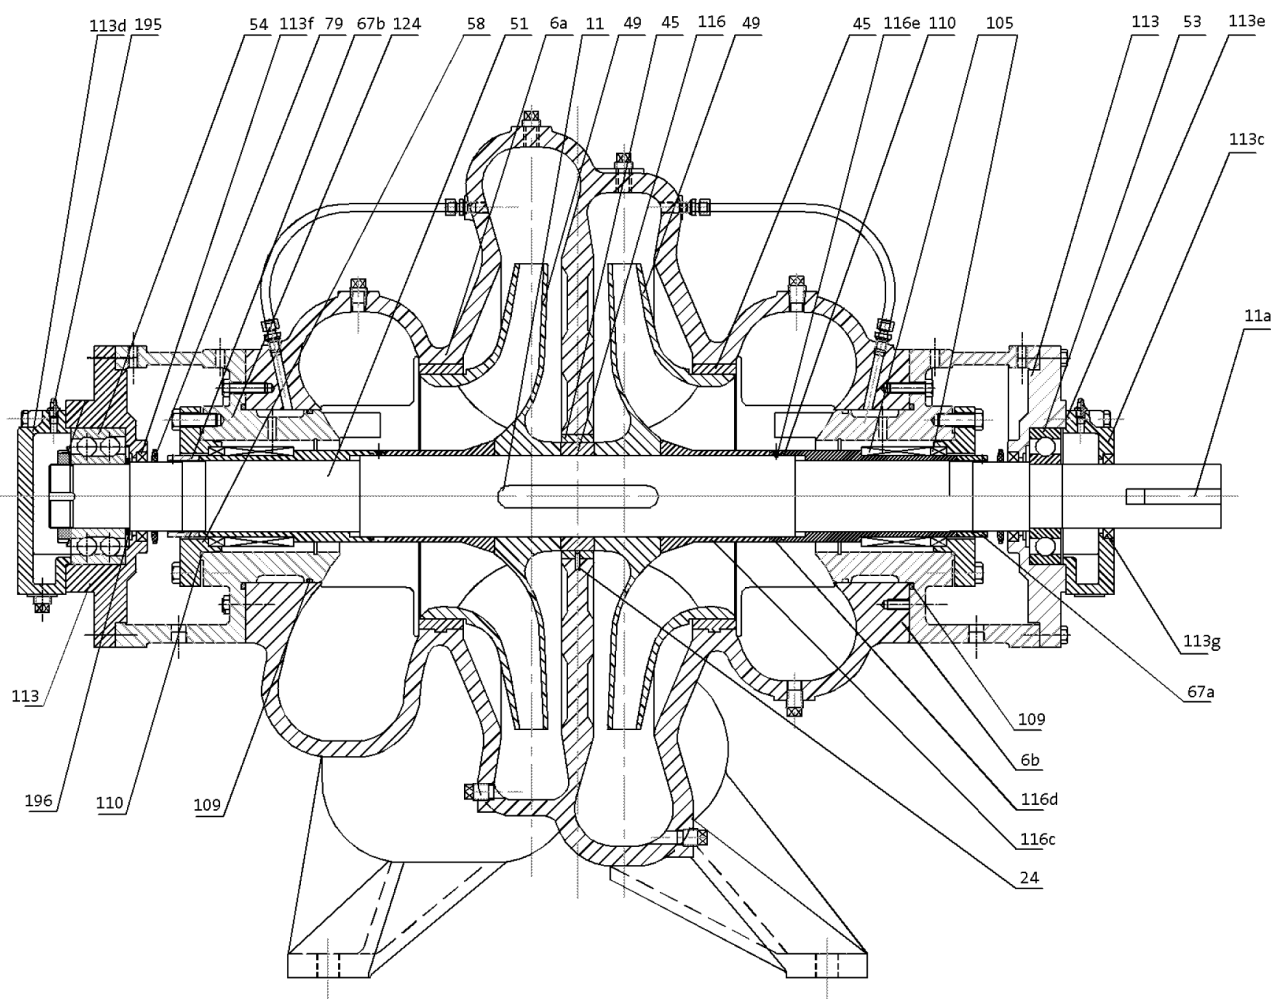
Вид в разрезе, тип конструкции 7, с торцевыми уплотнениями вала
